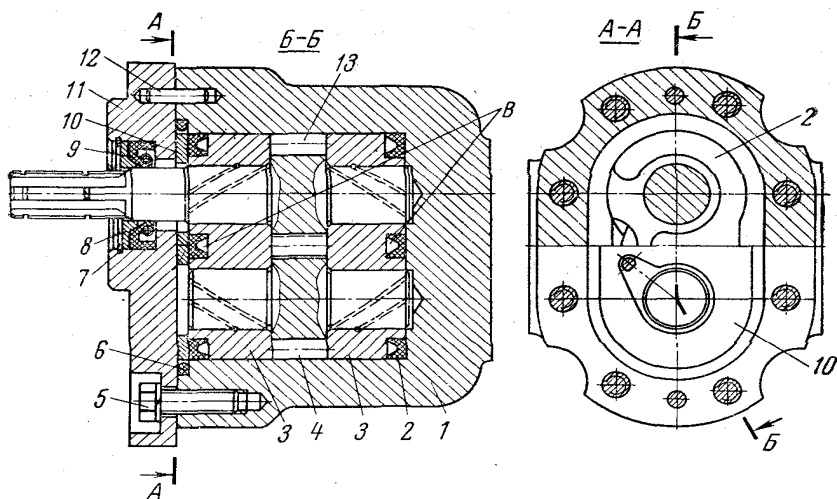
Шестеренный насос типа НШ-10: 1- корпус; 2- манжета фигурная; 3 обойма-подшипник; 4,13- ведомая и ведущая вал-шестерни; 5- винт; 6- кольцо резиновое; 7- кольцо стопорное; 8- кольцо опорное; 9- манжета; 10- пластина; 11- крышка; 12- штифт
